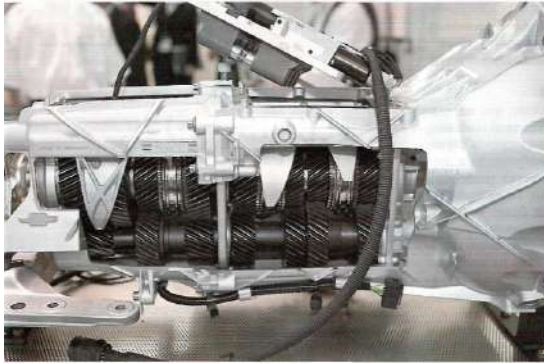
Автоматична система керування вальною коробкою передач БМВ М5
